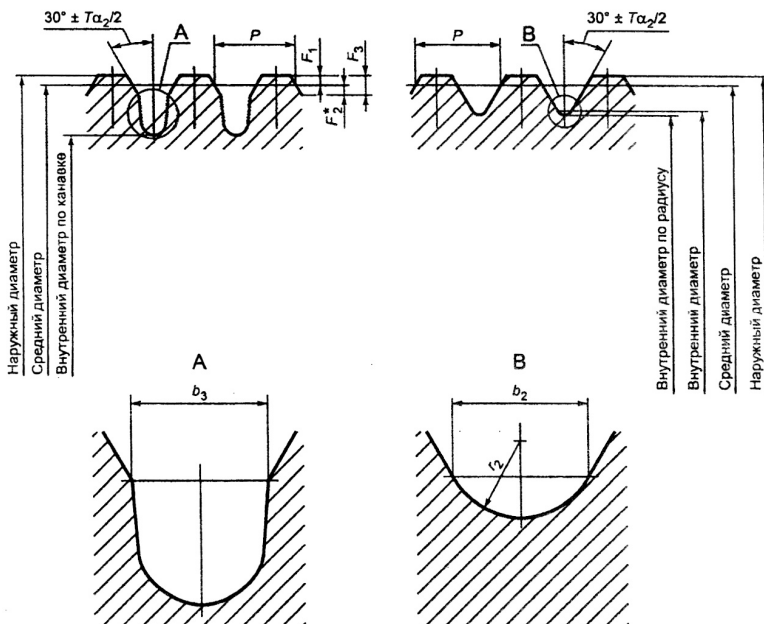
Укороченный профиль резьбы * Размер для справок
